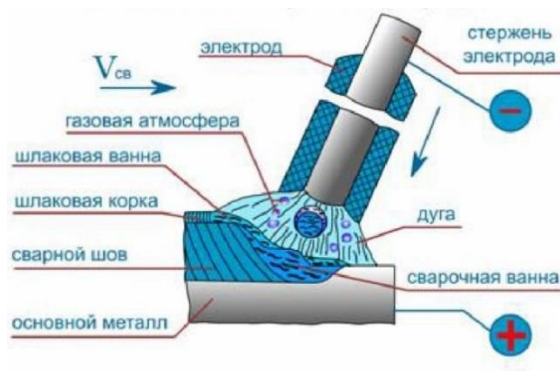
Схема выполнения ручной дуговой сварки
